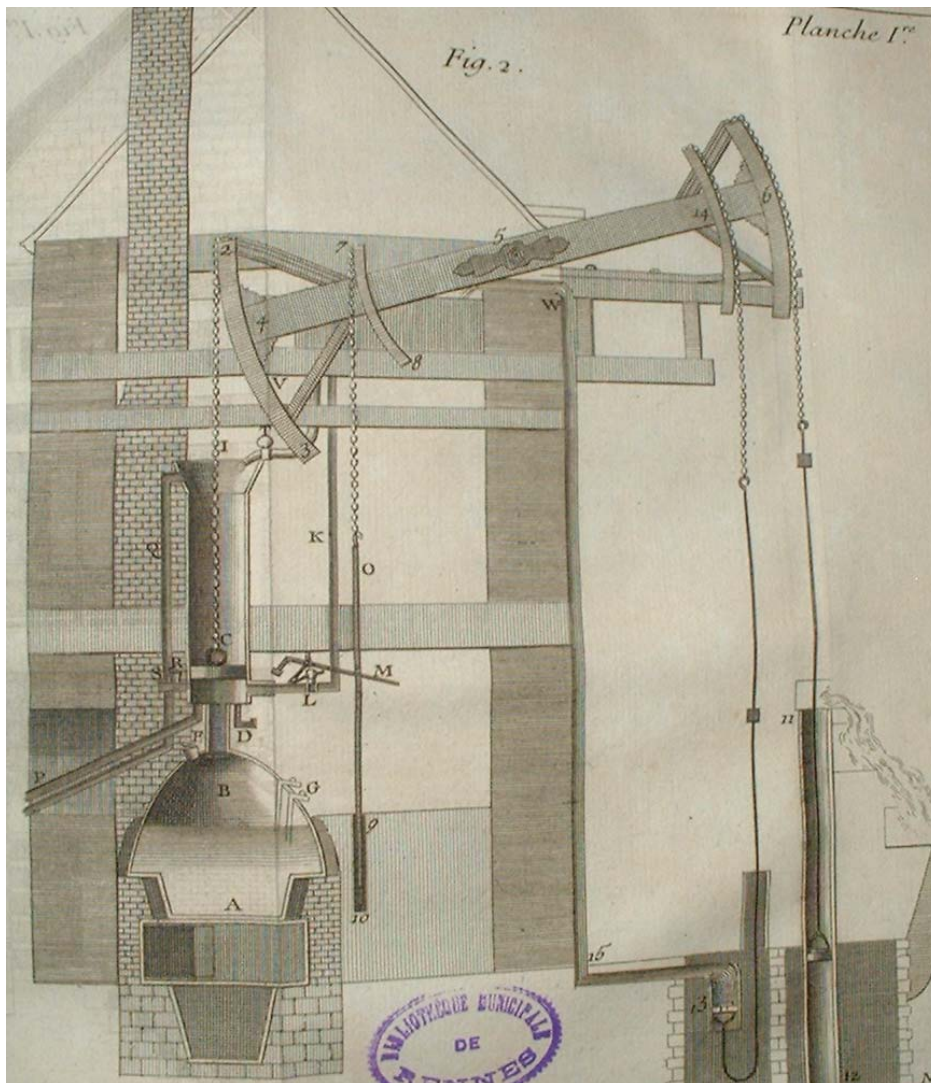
, machine hydraulique, Gallon, 20 x 31 cm.
